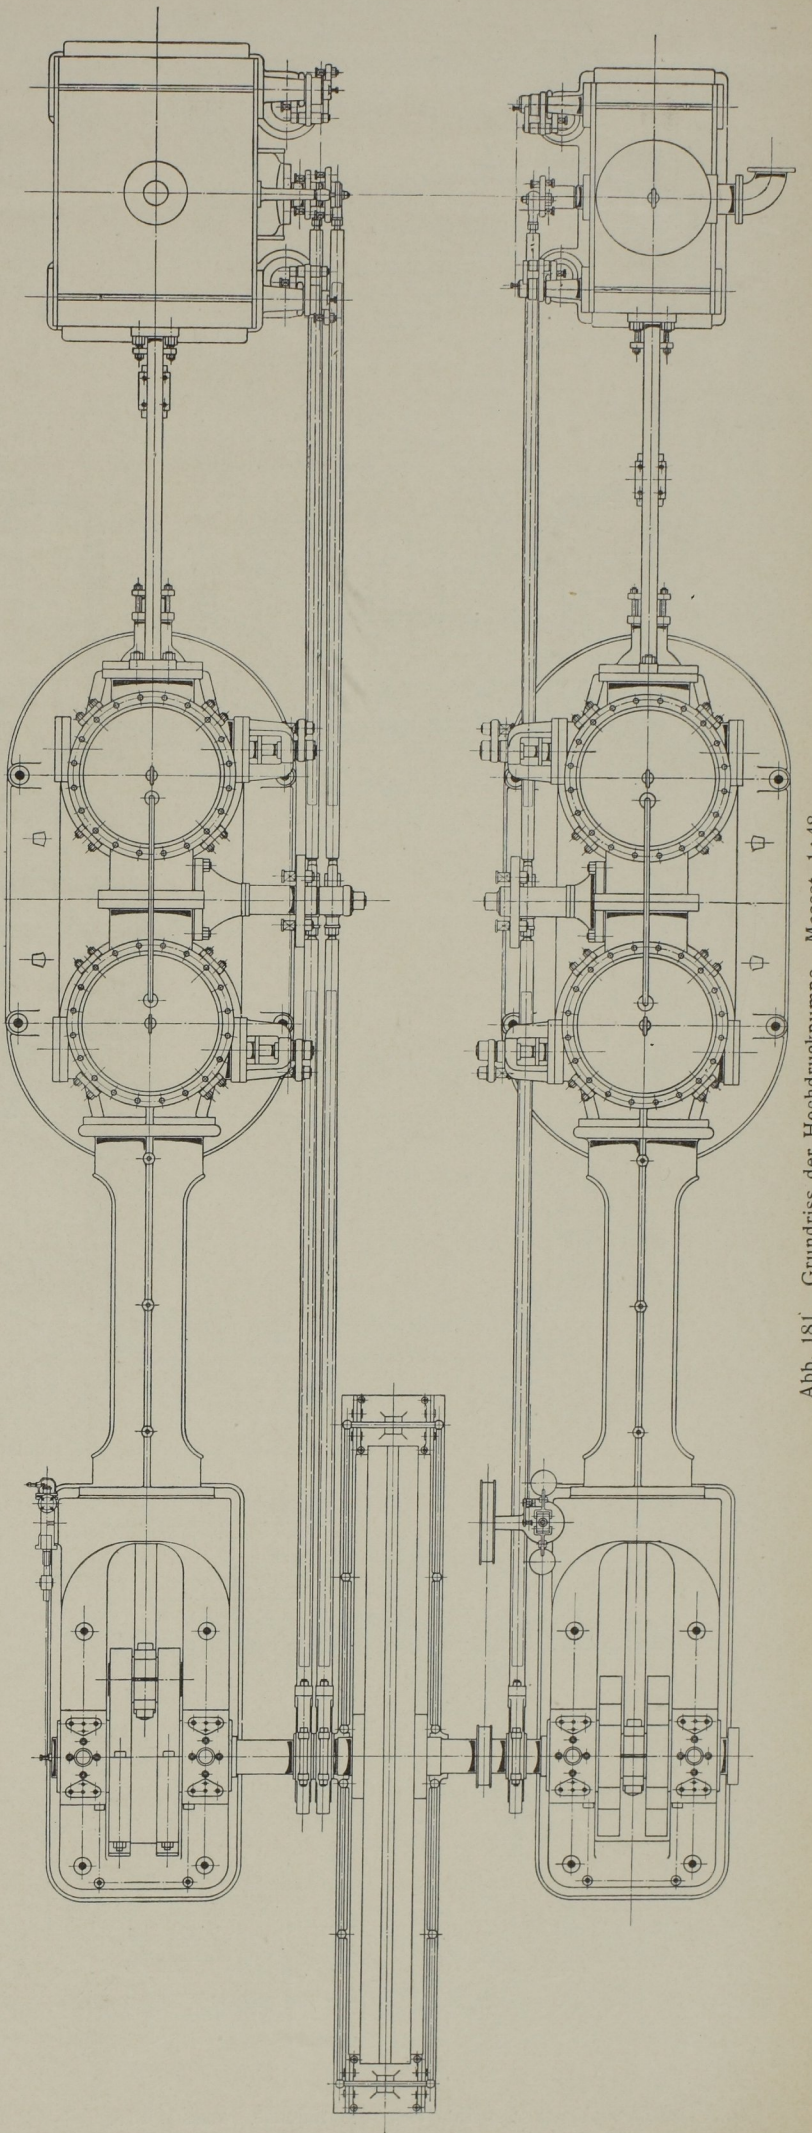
Grundriss der Hochdruckpumpe. Massst. 1 : 48.
